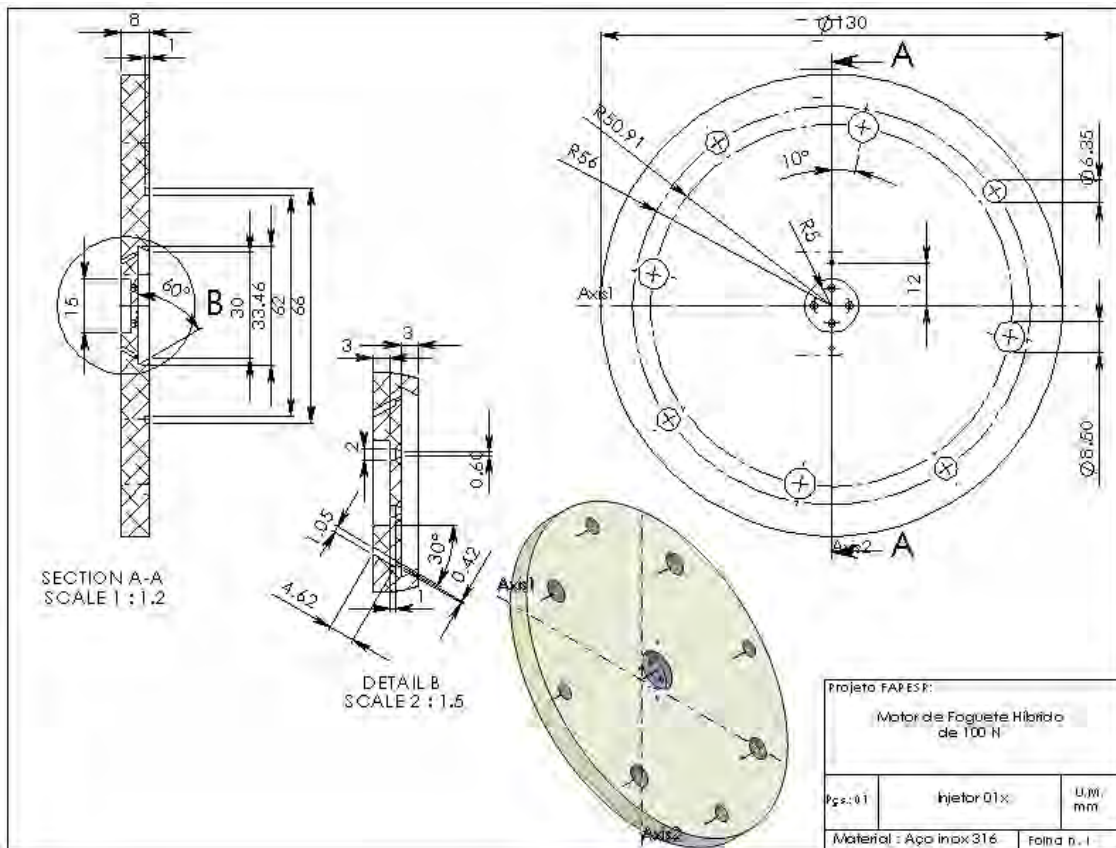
Desmontagem do injetor bipropelente, cotas do flange, injetor 01X, para posterior fabricação.
